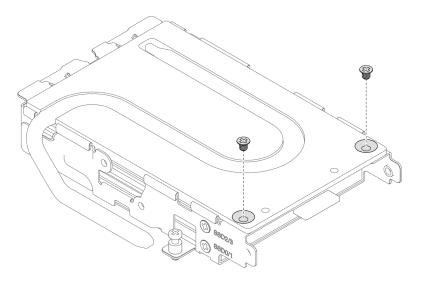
Entfernen der Schrauben vom Kühlkörper
